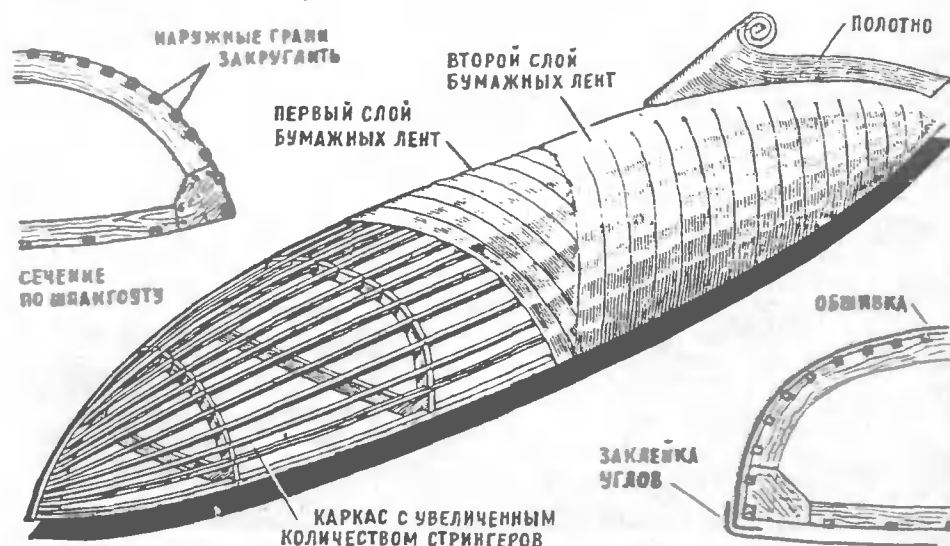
Изготовление обшивки корпуса байдарки (каяка) из крафт-бумаги.
